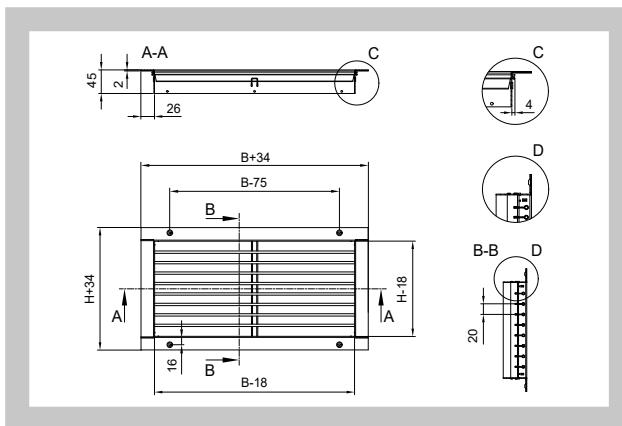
Feste Lamellen - Lamellenabstand 20 mm B > 600 mm
